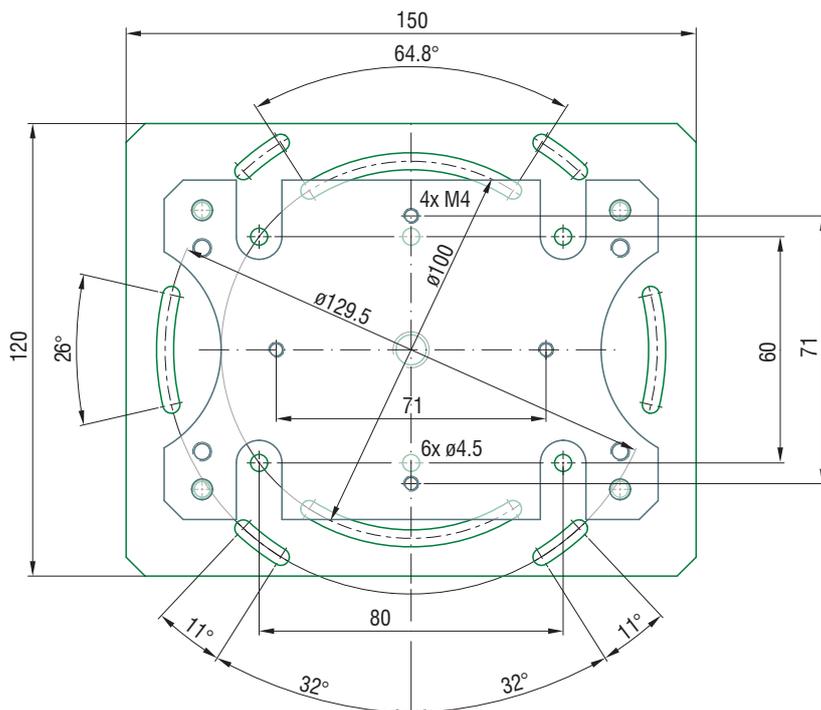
Maßzeichnung Montageplatte ILR-MP3800, Abmessungen in mm.
